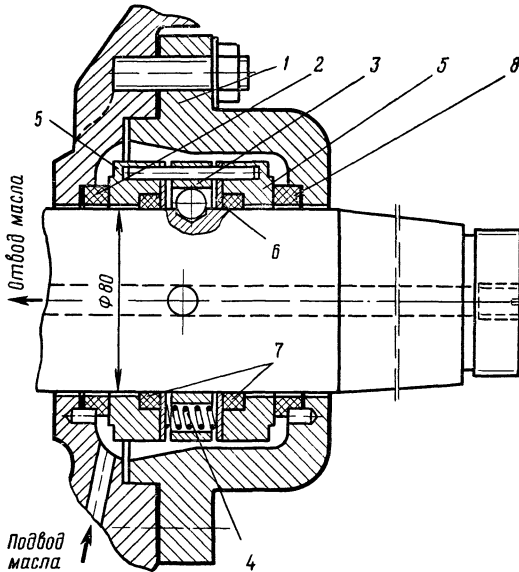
Сальник пружинный уплотнения конца вала (компрессор П80).
